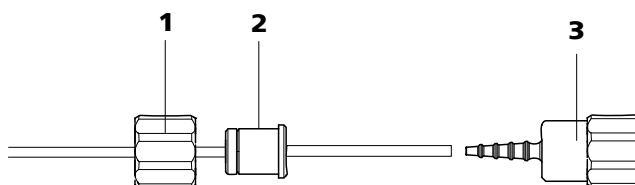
Instalación de una conexión de tubo de bomba sin filtro
